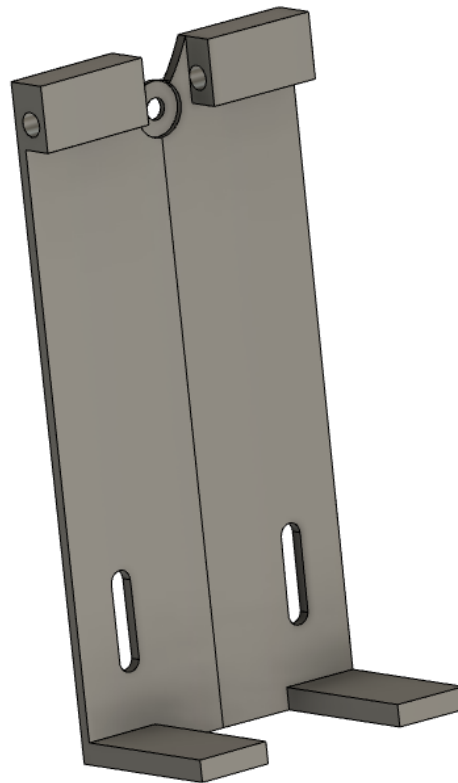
Disseny CAD del suport per al mesurador de profunditat
